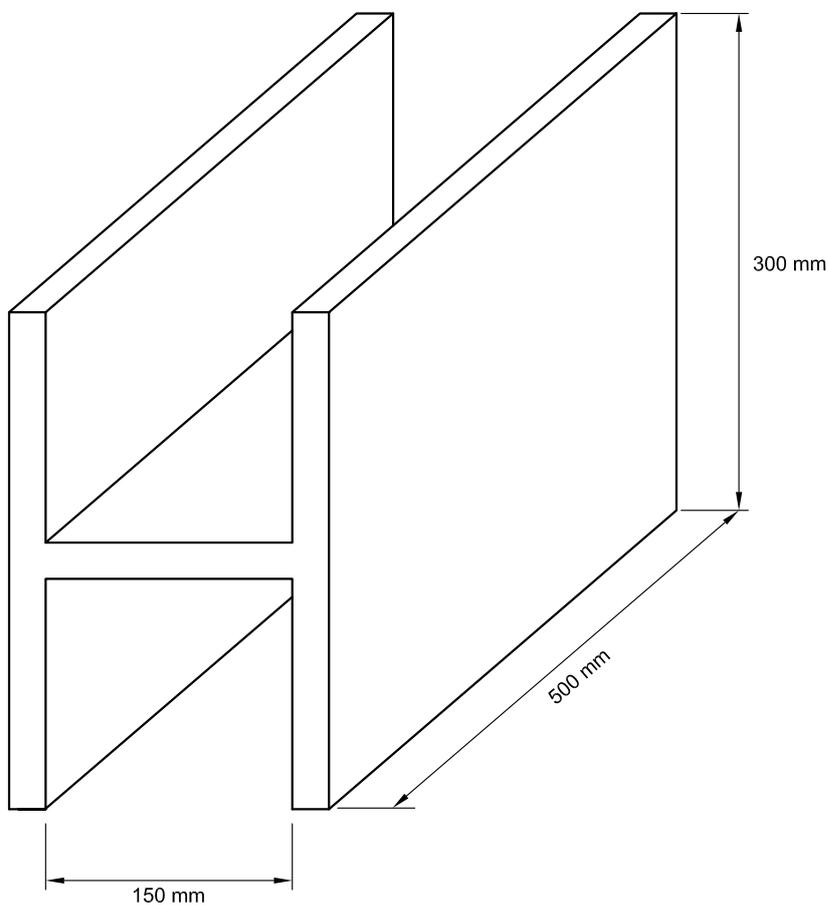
Perfil H para Ensaio de Medição de Espessura
